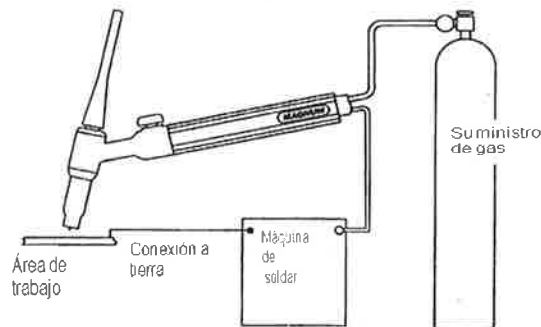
Esquema del equipo para la soldadura TIG.
